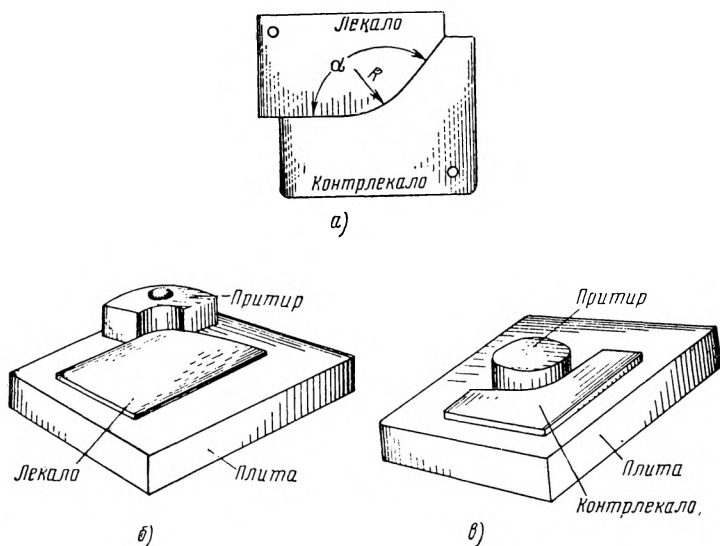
Схемы изготовления радиусно-углового лекала и контрлекала:
